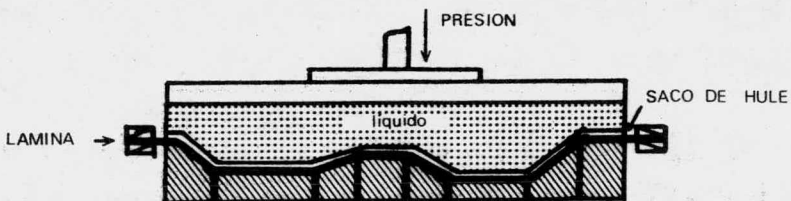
TERMOFORMADO CON MOLDES ENFRENTADOS UTILIZANDO UN SOLO MOLDE
